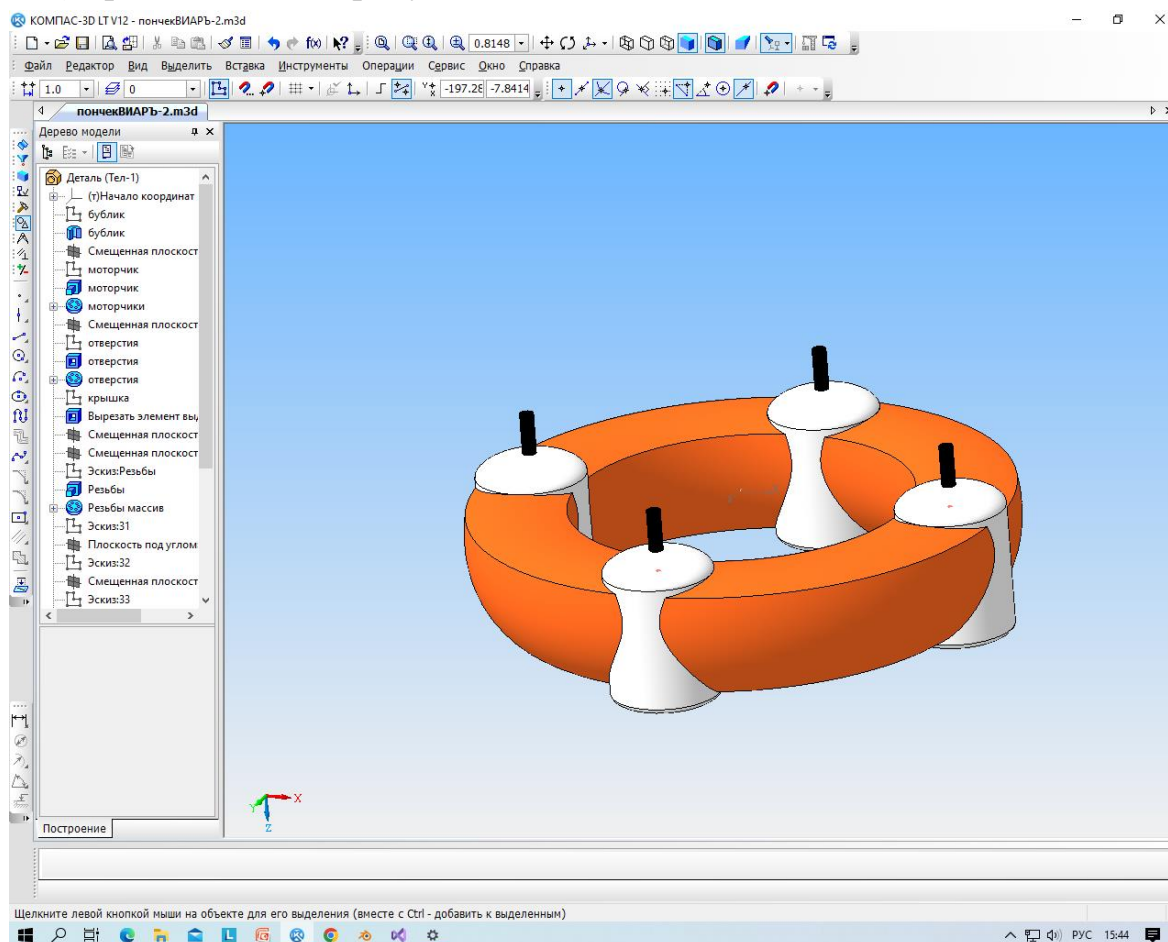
3D-модель плавающего квадрокоптера «Вихрь»
